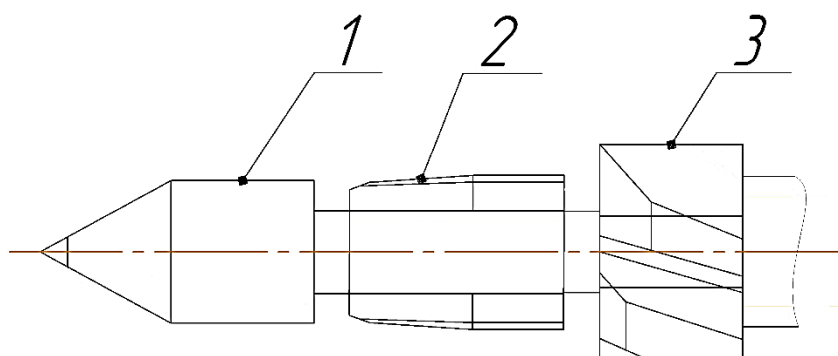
Схема конструкции комбинированного инструмента для формообразования резьбовых отверстий в заготовках из листового металла
